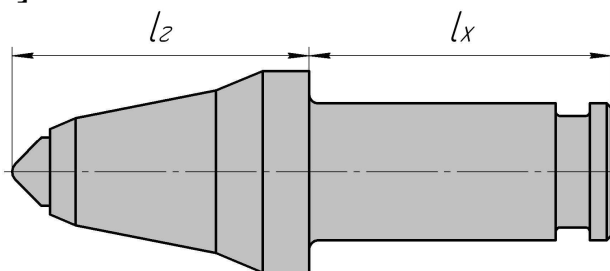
Унифицированный тангенциальный поворотный резец
